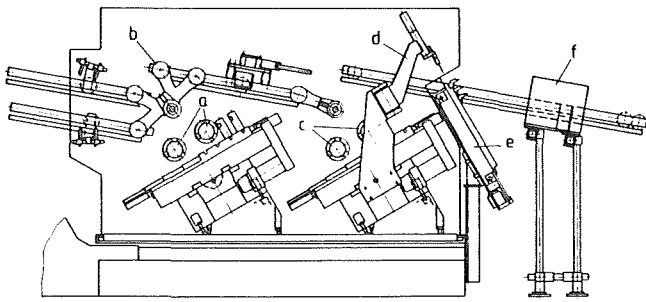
Flexibles NC-Frontdrehmaschinensystem zum Bearbeiten von Getrieberädern
